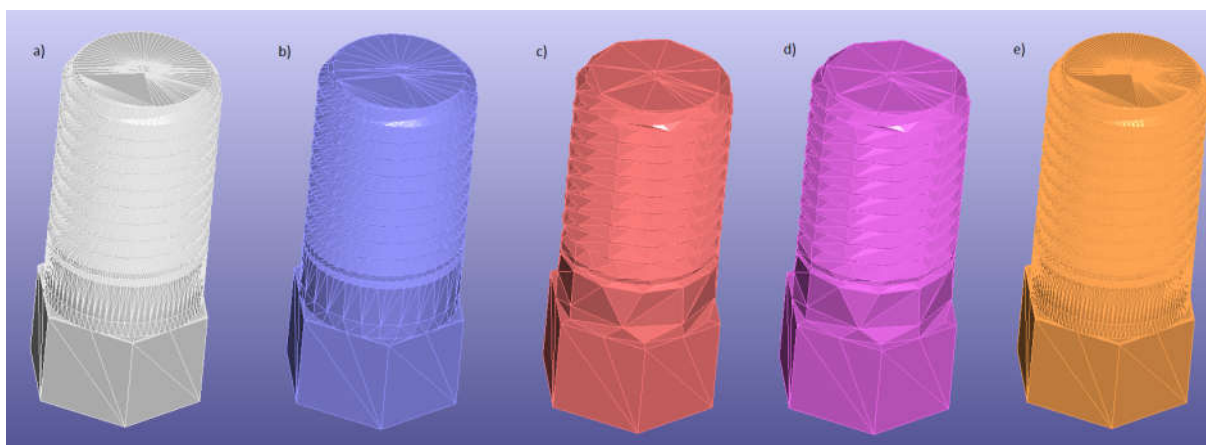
Widok zaprojektowanych modeli CAD [A14]
